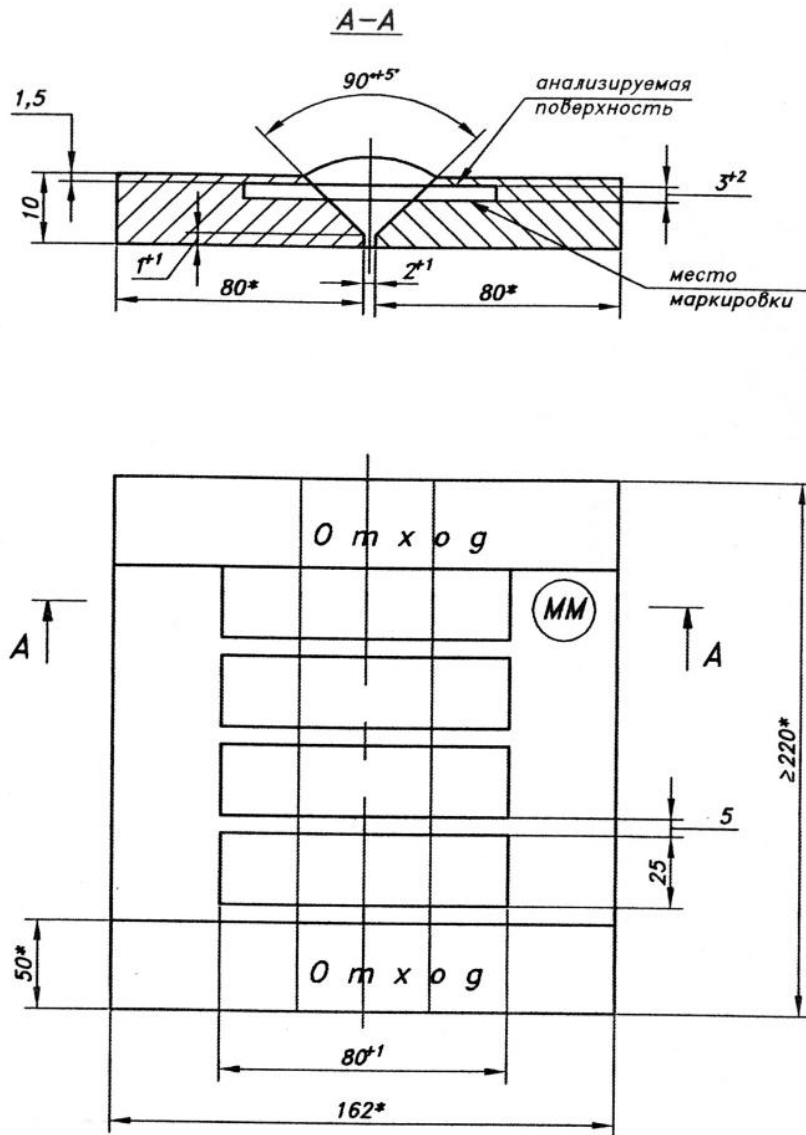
Типовая схема сварки пробы, выполненной проволокой аустенитного класса в среде защитных газов или под флюсом и вырезки заготовок образцов из металла шва
